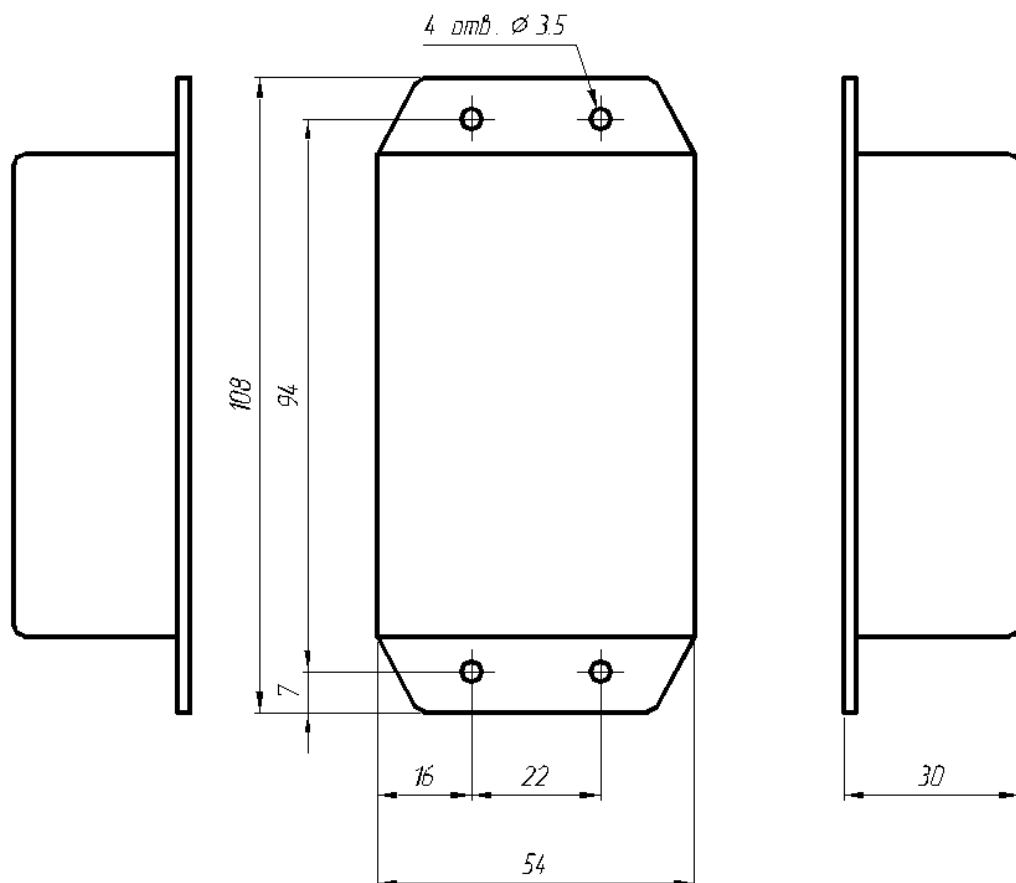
Габаритные и присоединительные размеры контроллера CGD-1
